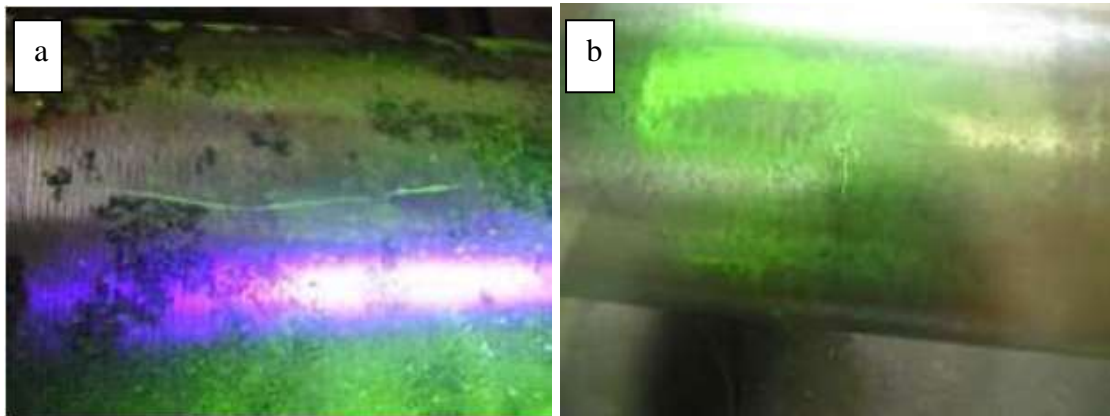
Detección mediante partículas magnetizables fluorescentes: a) fisura longitudinal, b) fisura transversal, [67].
